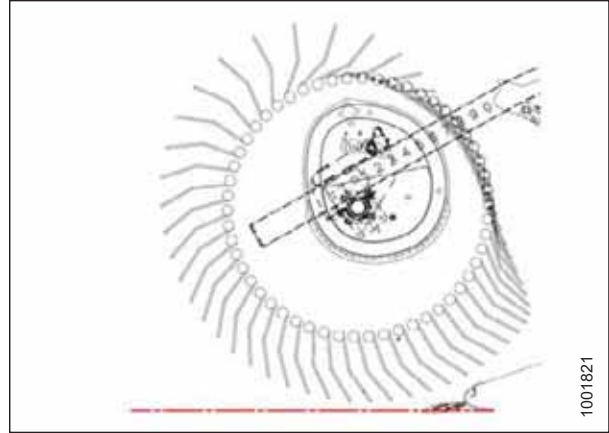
Вертикальний розріз пальця — положення 3
